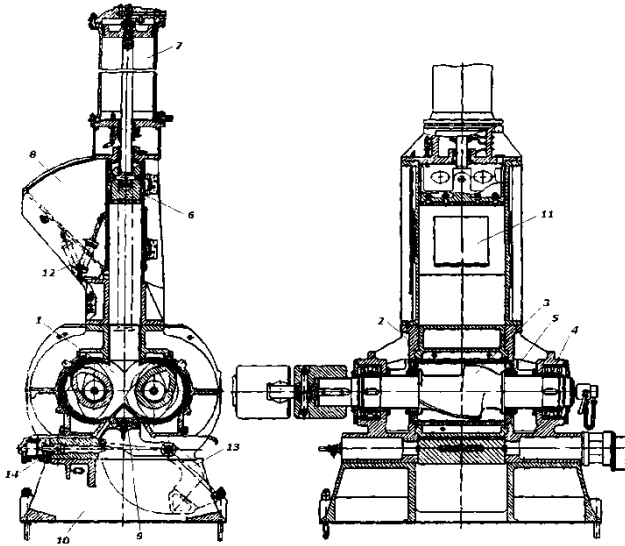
Змішувач закритого типу: 1 – камера змішувача; 2 – торцева стінка; 3 – ротор; 4 – підшипник кочення; 5 – ущільнювальний пристрій; 6 – верхній затвор; 7 – пневмоциліндр верхнього затвора; 8 – завантажувальний бункер; 9 – нижній затвор; 10 – станина; 11 – дверці; 12 – пневмоциліндр дверці; 13 – шарнірний важіль; 14 – гідроциліндр
